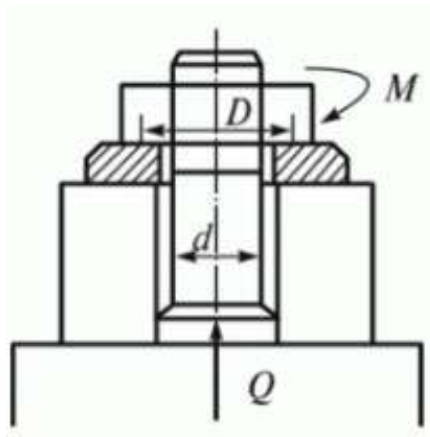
Приклад гвинтового затискача заготовки
